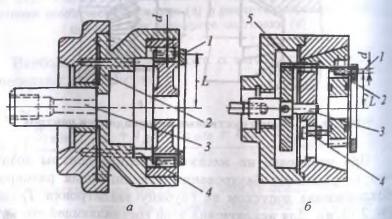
Патроны для установки зубчатых колес по рабочим поверхностям
